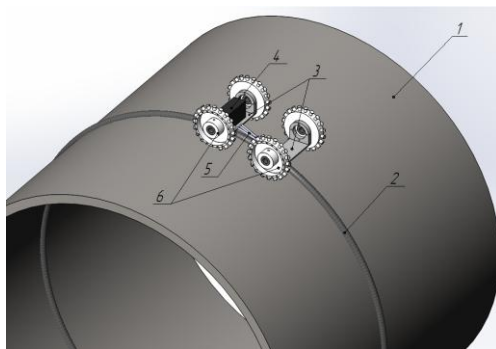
Автоматизированное устройство для проведения ультразвуковой дефектоскопии сварных труб: 1 – металлическая труба, 2 – сварной шов, 3 – элементная база, 4 – блок управления и детекторы, 5 – соединительный кабель, 6 – магнитоходные колеса
